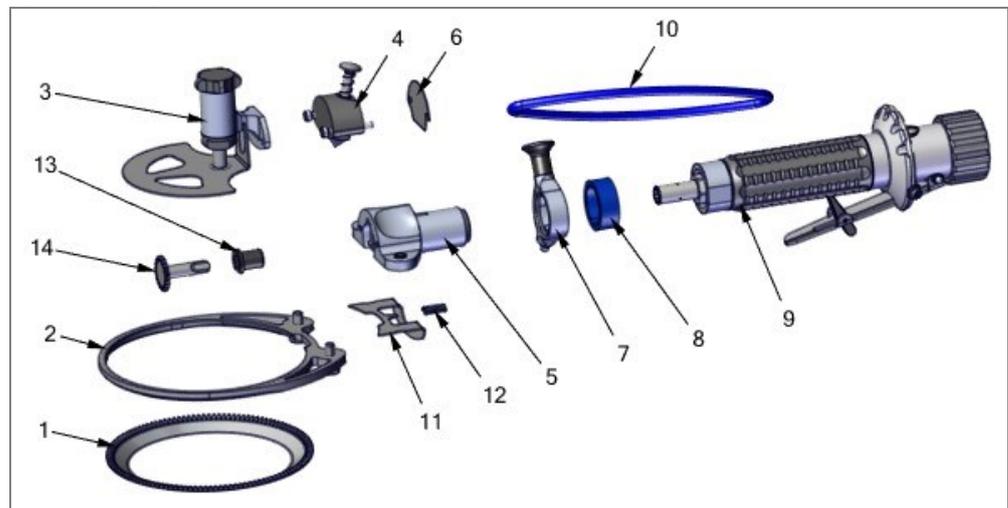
Trimmer pneumatique 128_evo3 (exemple)
